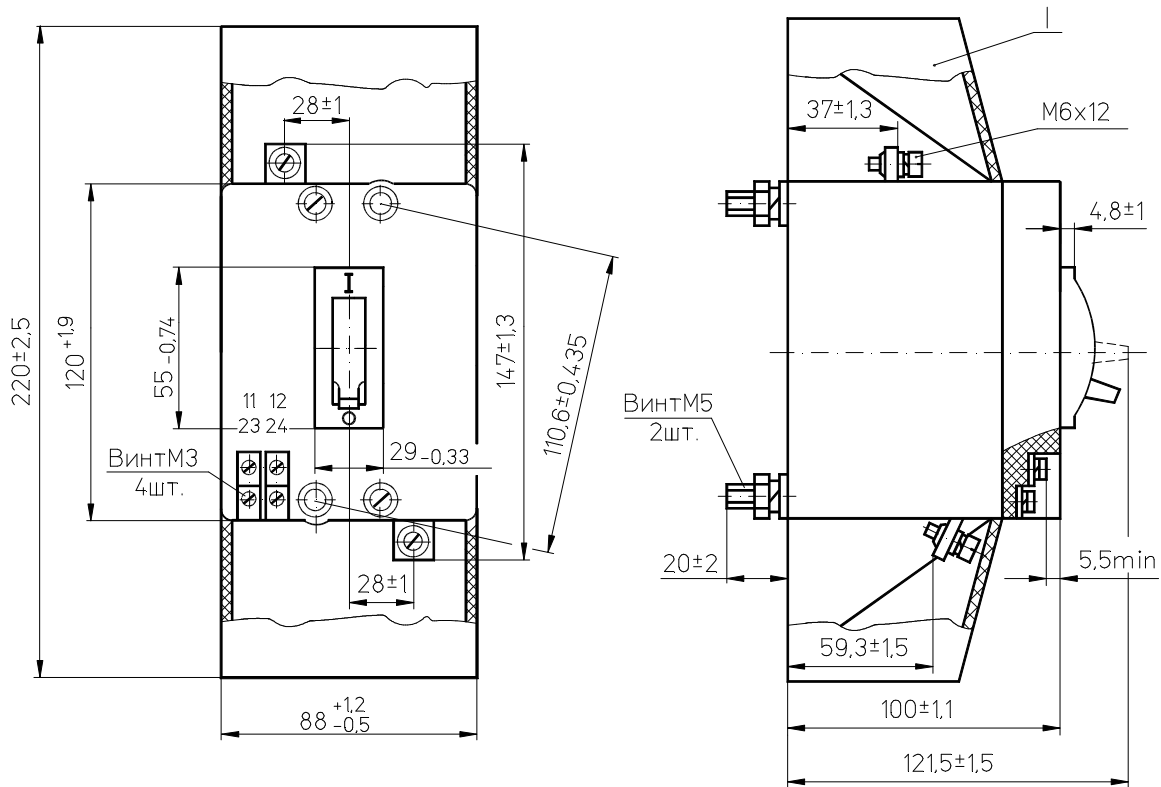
Сверление отверстий под винты крепления трехполюсного выключателя
